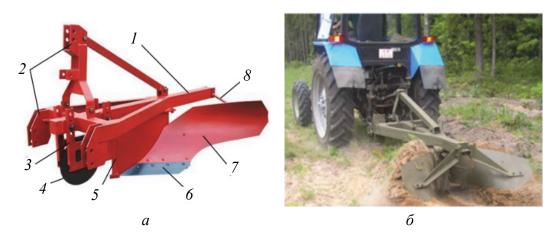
Плуг лесной ПКЛ-70Д: a — схема устройства; δ — общий вид агрегата; l — рама; 2 — навеска; 3 — кронштейн; 4 — дисковый подрезной нож; 5 — нож корпуса; δ — лемех; 7 — отвал; 8 — распорка отвалов
